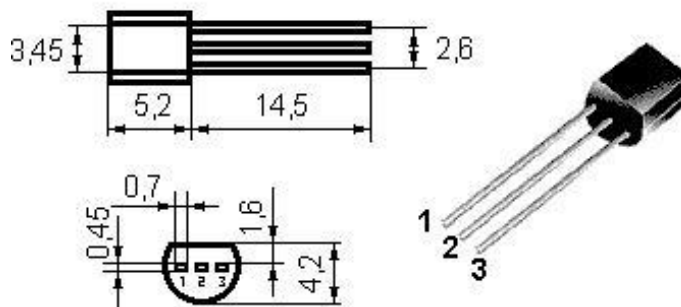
Габаритні розміри транзистора 2N3904BU
